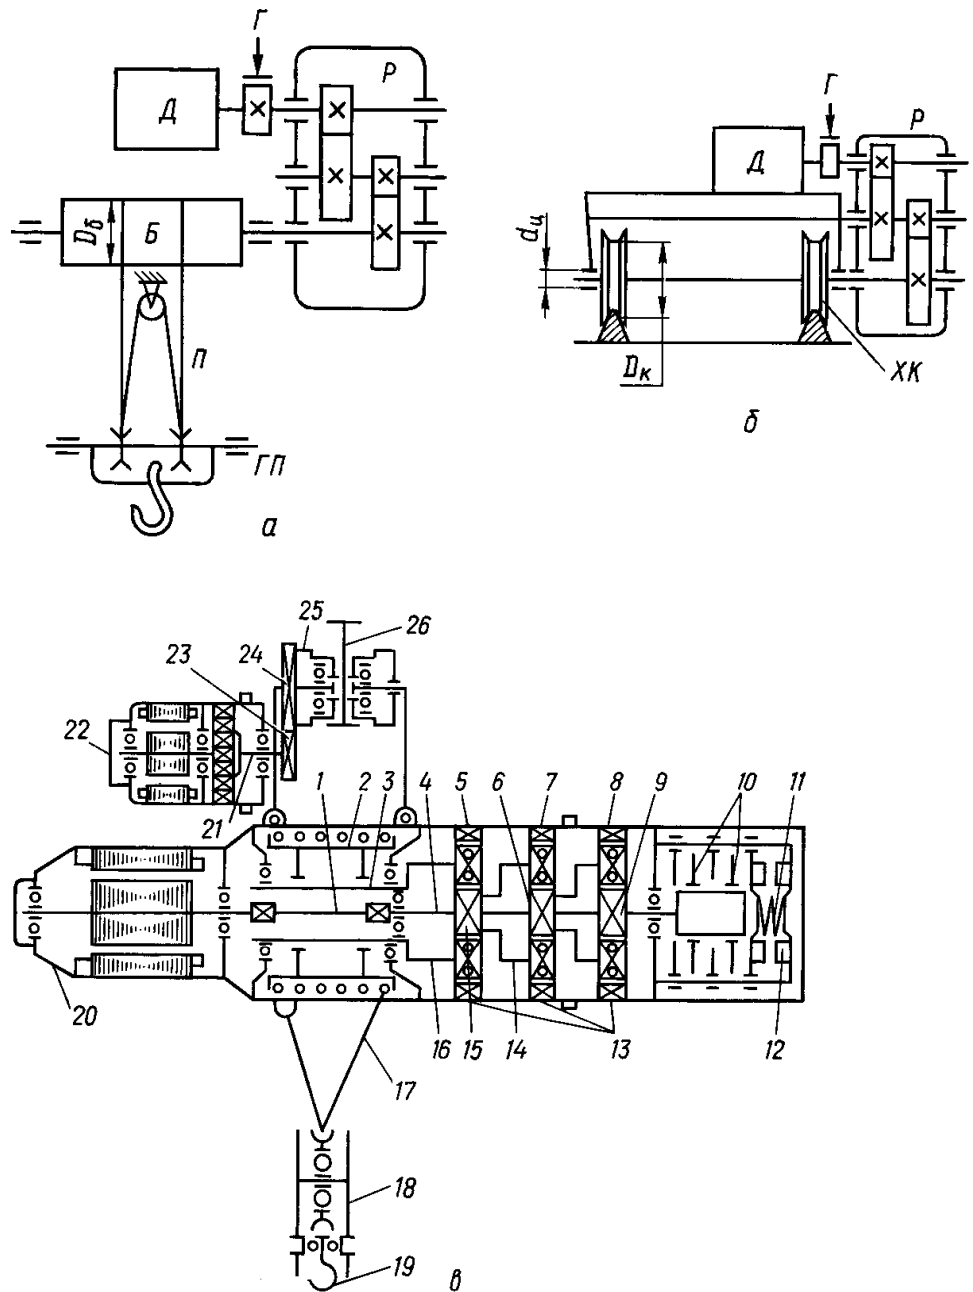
Кінематичні схеми кранових механізмів: а - однокінцевої підйомної лебідки; б - механізму переміщення; Д - двигун; Г - гальмо; Р - редуктор; Б - барабан; П - поліспасть; ГП - гакова підвіска; ХК - ходове колесо; в - талі ТЗП-1; 1 - проміжний вал; 2 - робочий барабан; 3 - порожнистий вал; 4 - робочий вал; 5, 7, 8 - сателіти; 6, 9, 15 - сонячні шестерні; 10 - гальмівні диски; 11 - гальмівна пружина; 12 - електромагніт; 13 - блочні шестерні; 14, 16, 21 - водила; 17 - канат; 18 - підвіска; 19 - гак; 20 -
